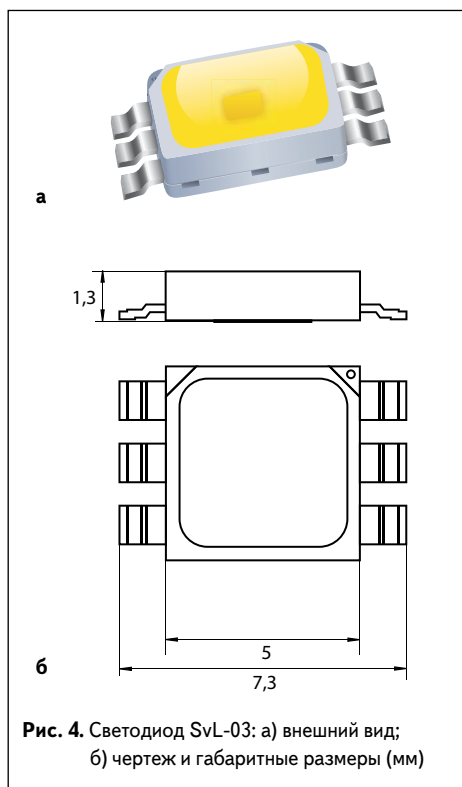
Светодиод SvL-03: а) внешний вид; б) чертеж и габаритные размеры (мм)
